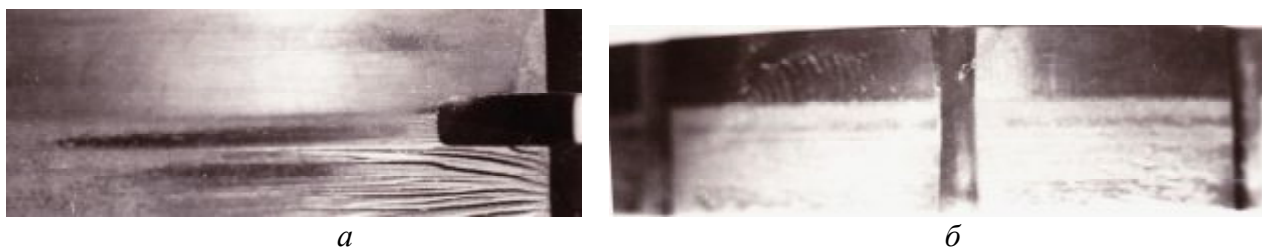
Фотографии рабочей поверхности твердосплавной колодочки с бороздками, образованными абразивными зернами (а) и ролика (б) с прерывистой рабочей поверхностью после 75000 нагружений
